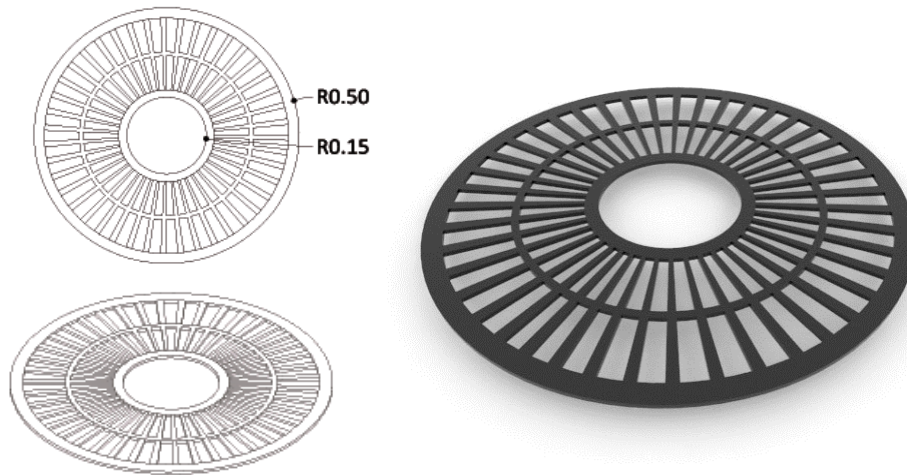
Planimetría y render, rejilla metálica 1. Fuente: grupo investigación.
